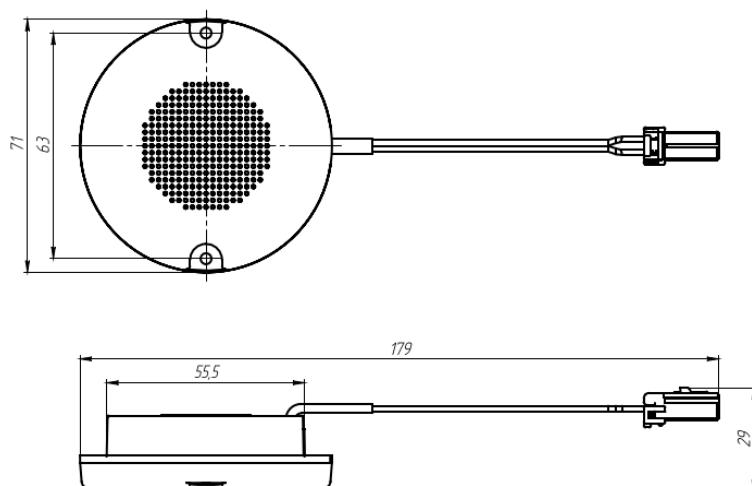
Габаритный чертёж Громкоговорителя ГМ-2-01
